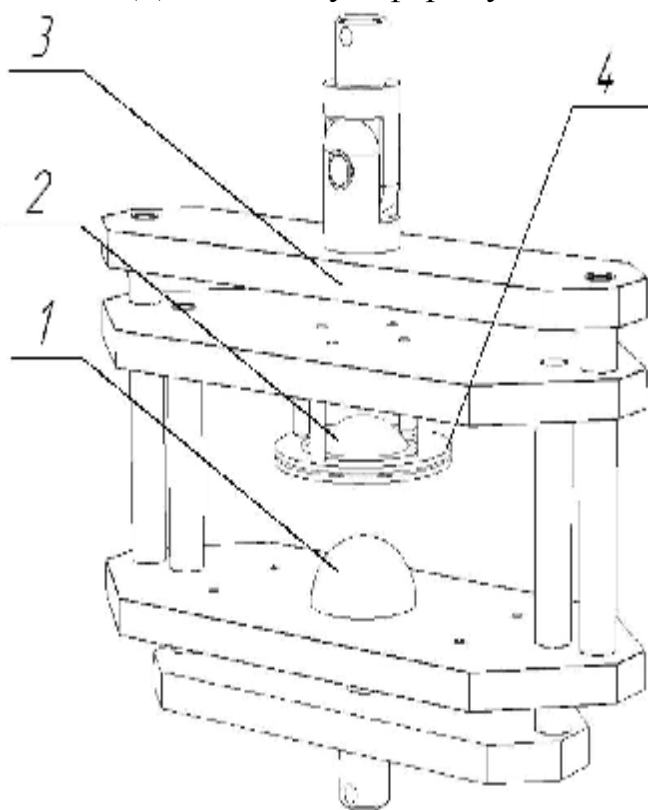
Внешний вид приспособления для двухосного растяжения
